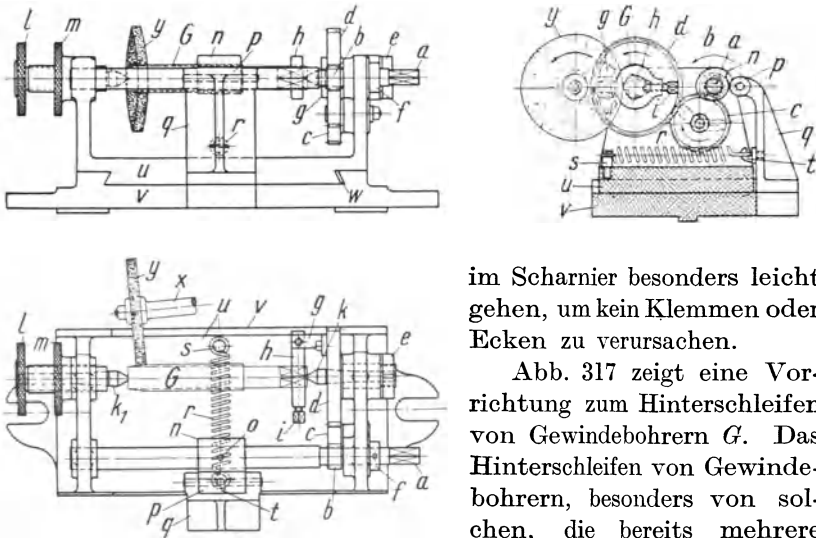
Hinterschleifvorrichtung für Gewindebohrer.
